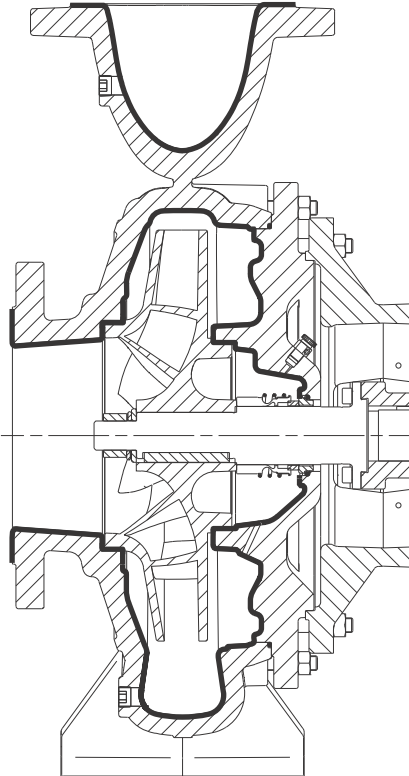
Schnittzeichnung von Pumpen mit einer Beschichtung für gechlortes Wasser
